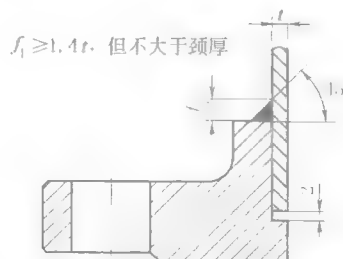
承插焊法兰与钢管的焊接连接
